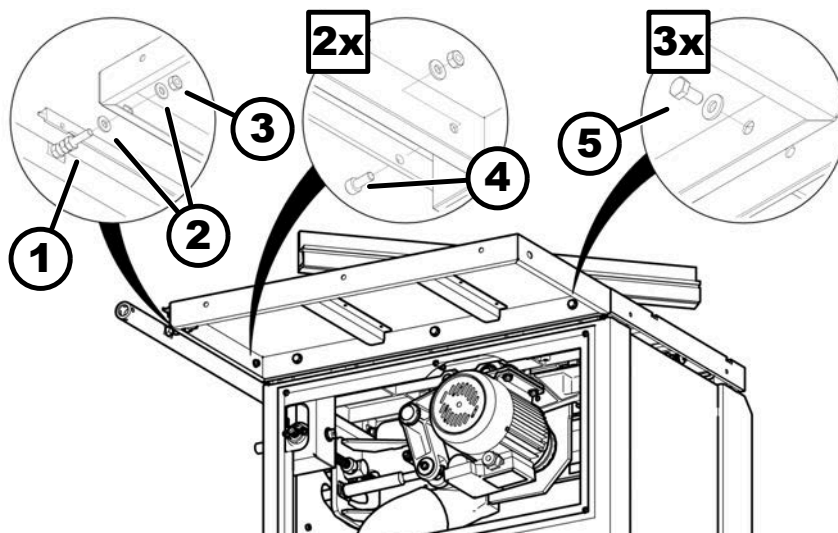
Montage de l'élargissement de coupe - variante 610
